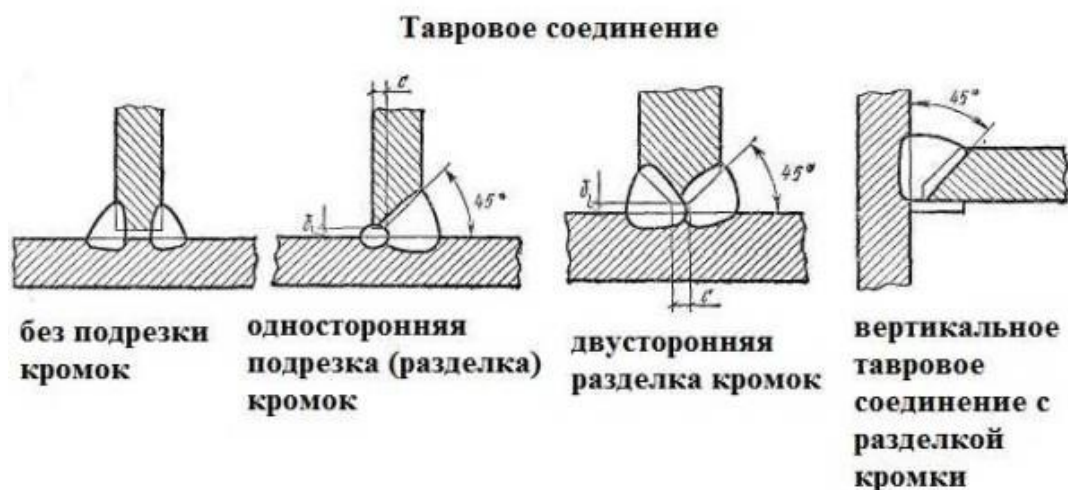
Типы сварных швов: тавровое соединение с разделкой (обрезкой) кромок и без
